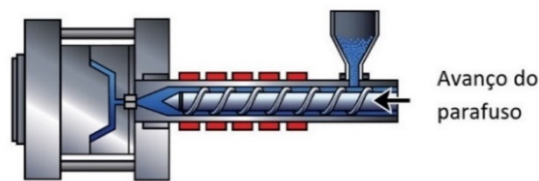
Ilustração da etapa de injeção, durante o ciclo de moldagem por injeção [4].
